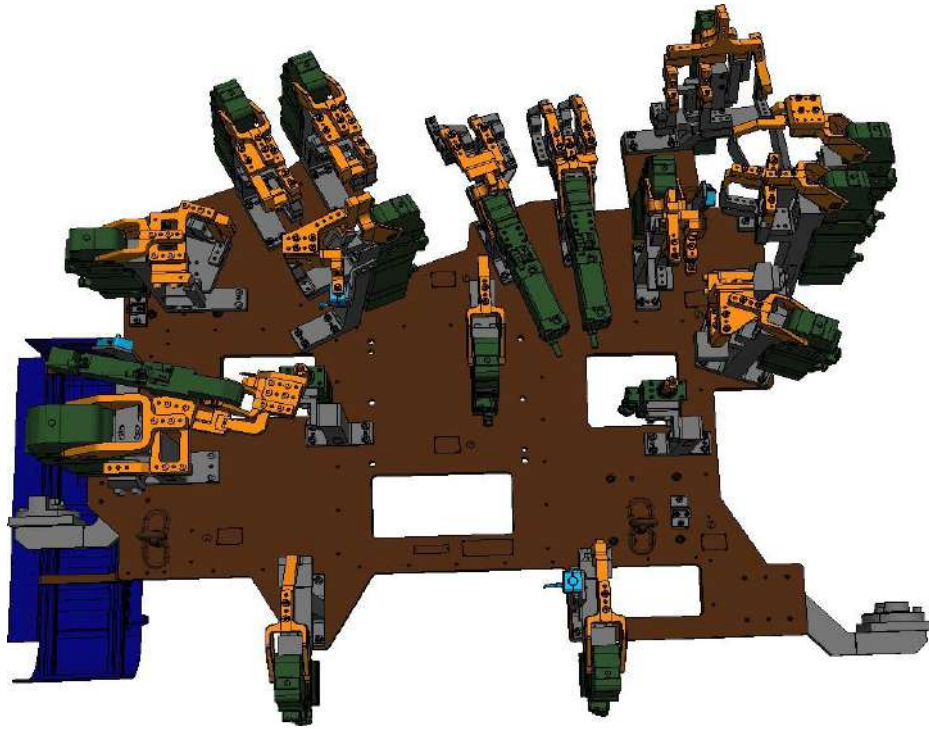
Позиціонуєча станція для контактного зварювання
